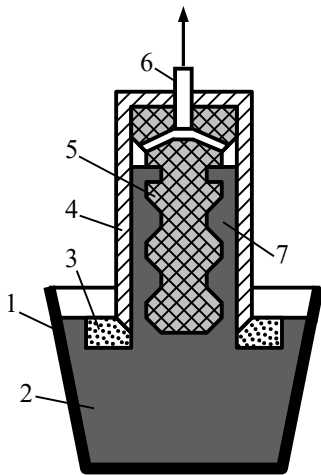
Виготовлення виливка литтям із протитиском:
